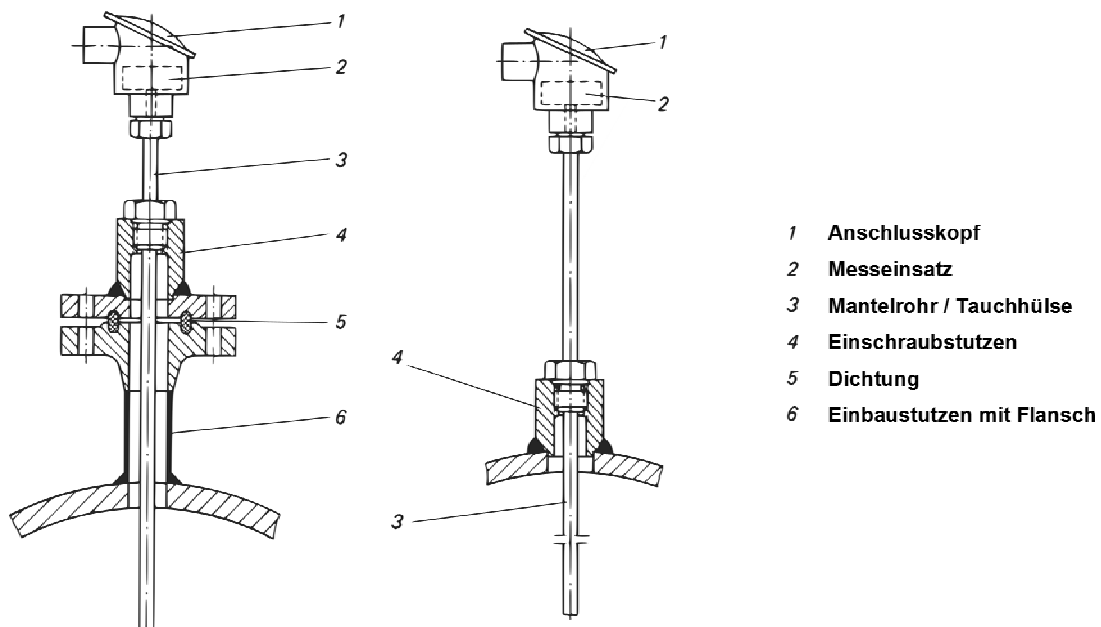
Messanordnung mit Schutzrohr (rechts: Einschraubstutzen; links: Flansch mit Einschraubstutzen und Zwischenflansch).
